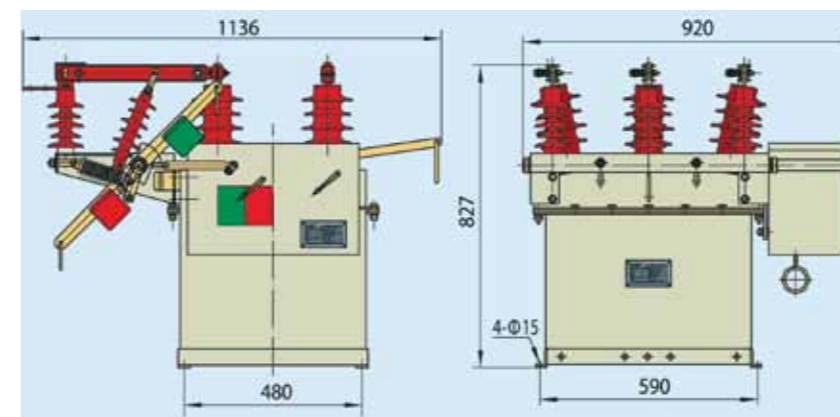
Выключатель ZW8-12 с разъединителем
